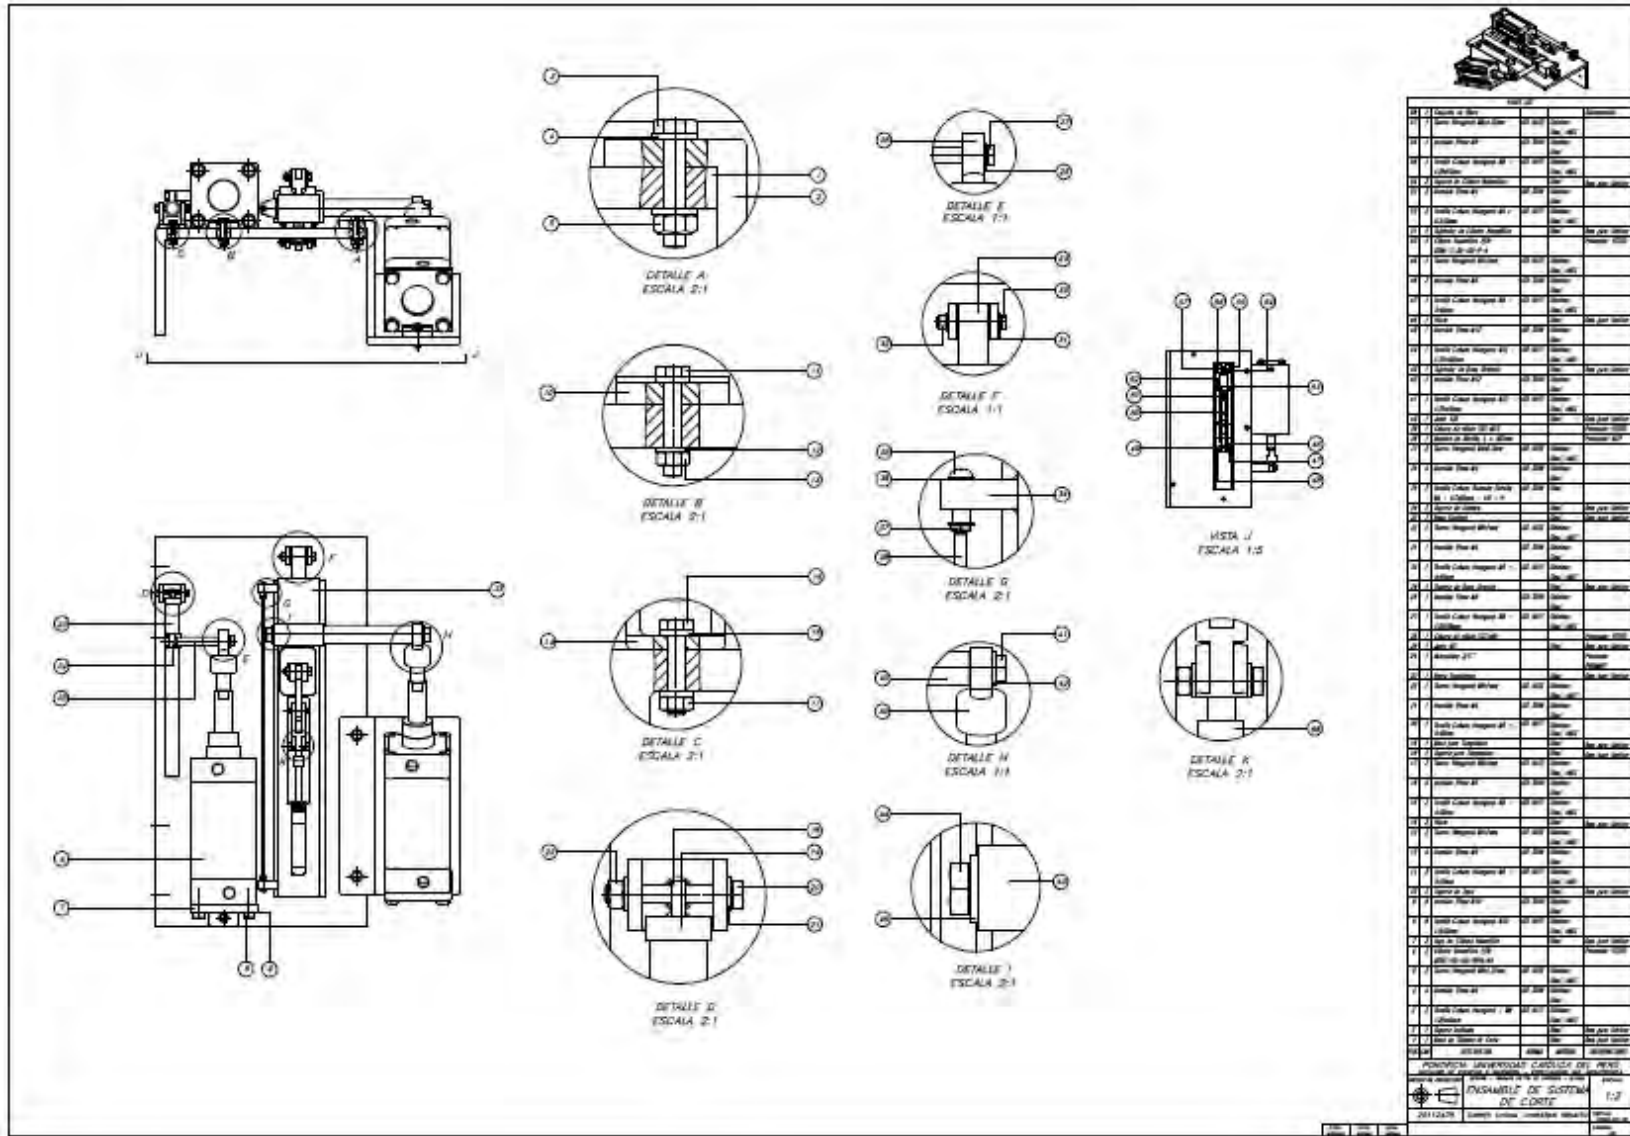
Sistema de Corte de film. Plano. Fuente: Propia.
